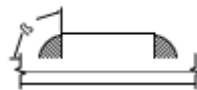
b. Unión soldada: Unión en solape [6]
